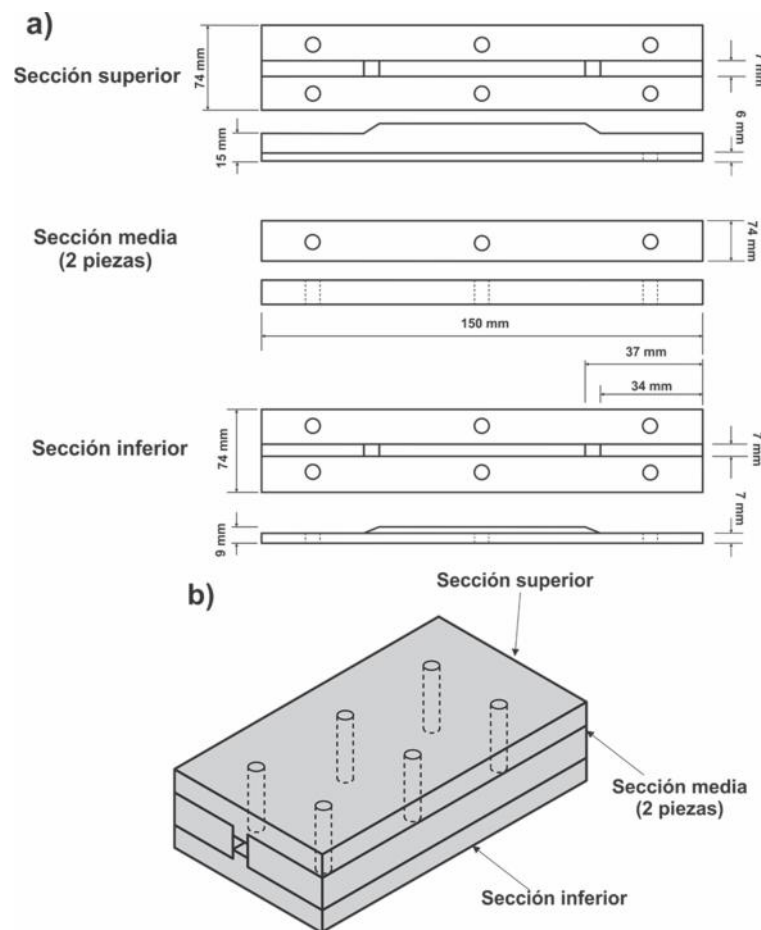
Esquema del molde utilizado para fabricar probetas de materiales compuestos a tensión. a) Piezas que conforman el molde, b) conjunto armado.
